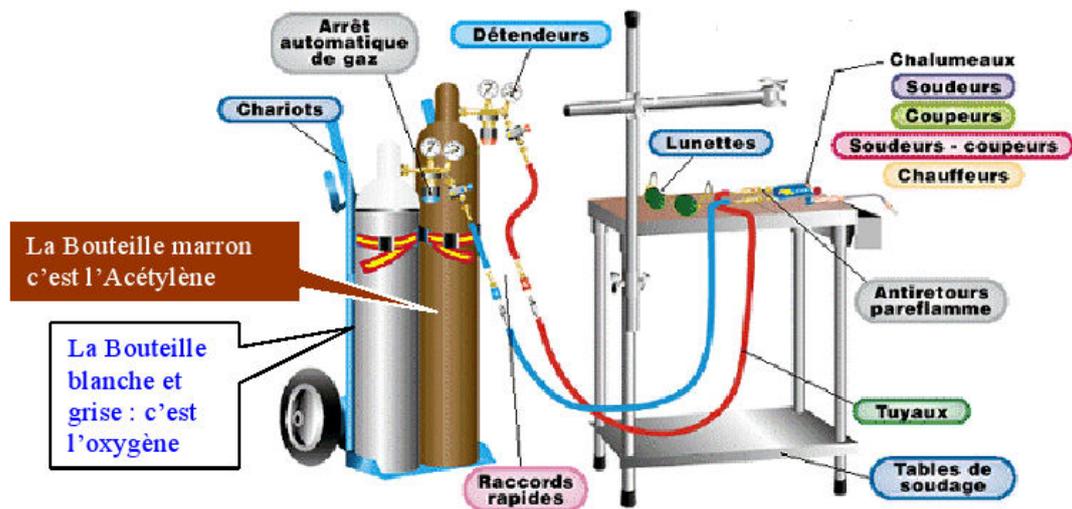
Principe de soudage oxyacétylénique [7].
